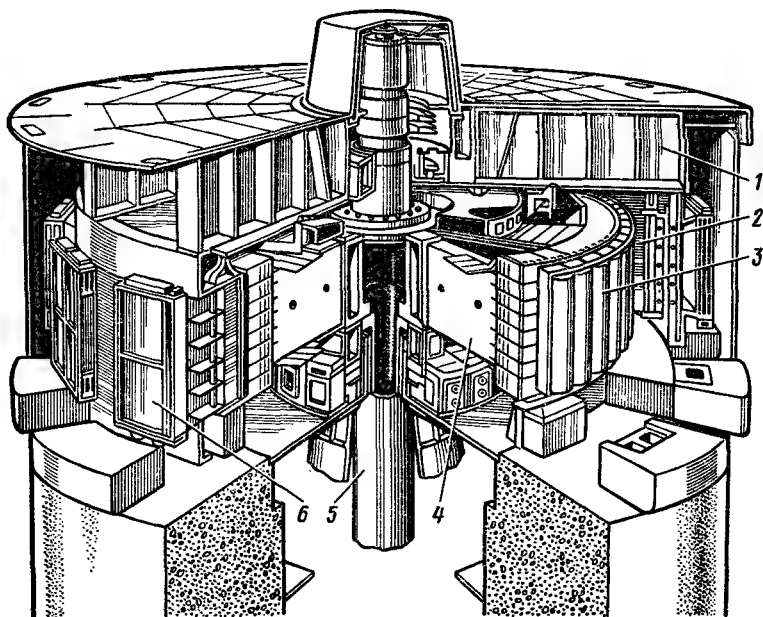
Общий вид гидрогенератора с вертикальным расположением вала:
